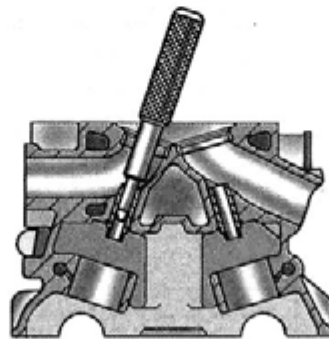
Выпрессовка направляющих втулок клапанов
